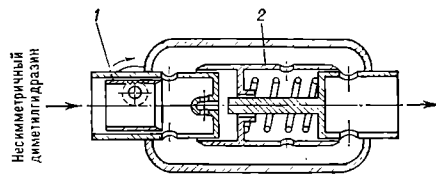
Регулятор расхода для газогенератора ЖРД РД-253: 1 — задающее устройство с приводом от электродвигателя; 2 — золотник стабилизирующего устройства
